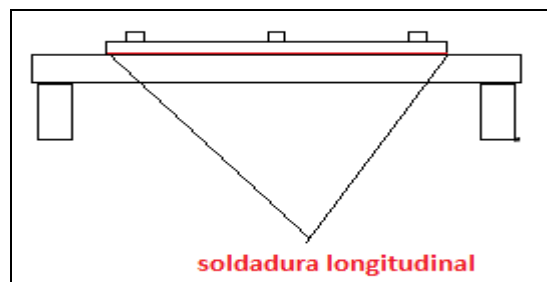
VISTA LATERAL DE LA SOLDADURA EN EL MONTAJE.
